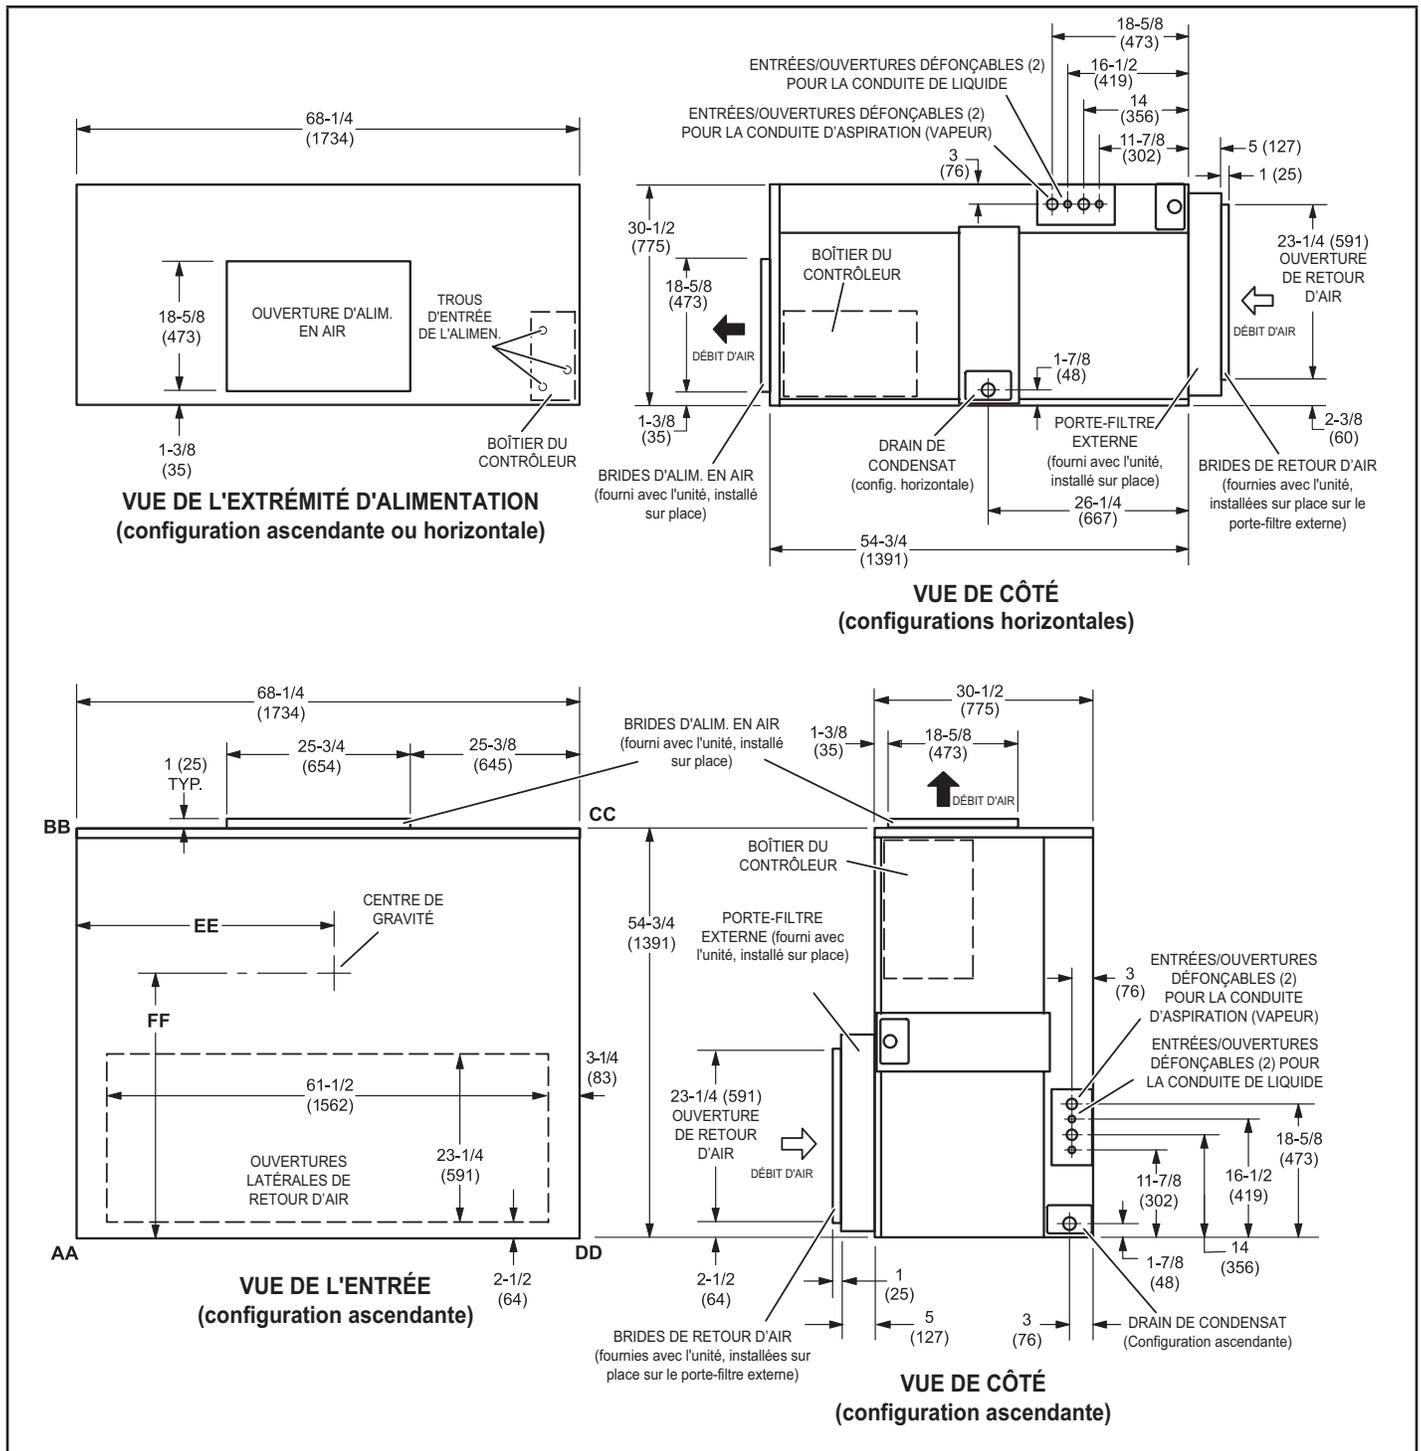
Dimensions de l'unité EL120-150KA – pouces (mm)
